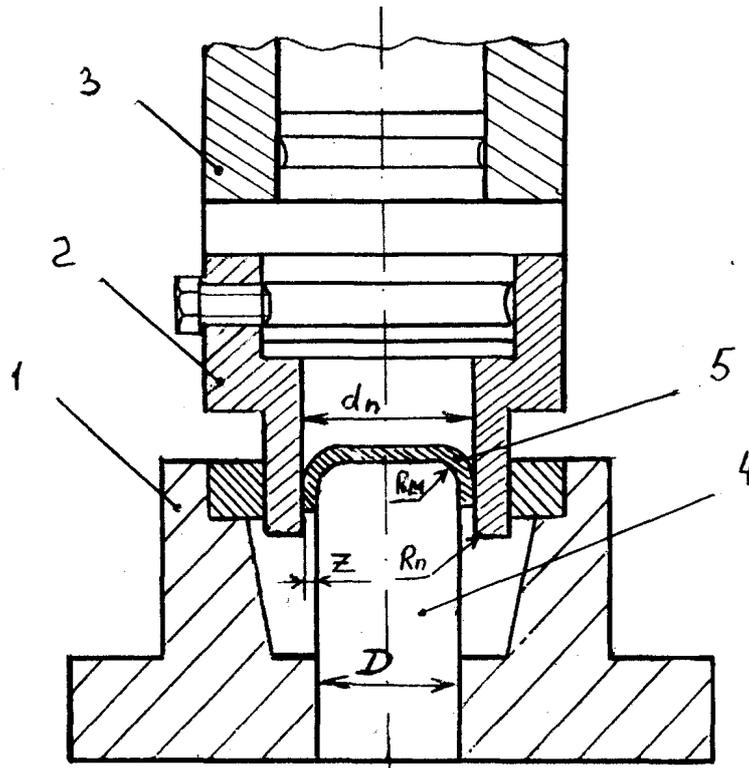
Схема получения детали «Копачок» методом холодной листовой штамповки
